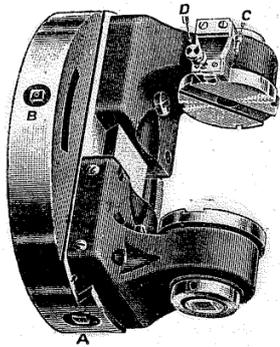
Chuck pour robinets, avec mâchoires à diviseur C et fixateur D, montées sur billes, et que l'on fait tourner par B sans les desserrer.
